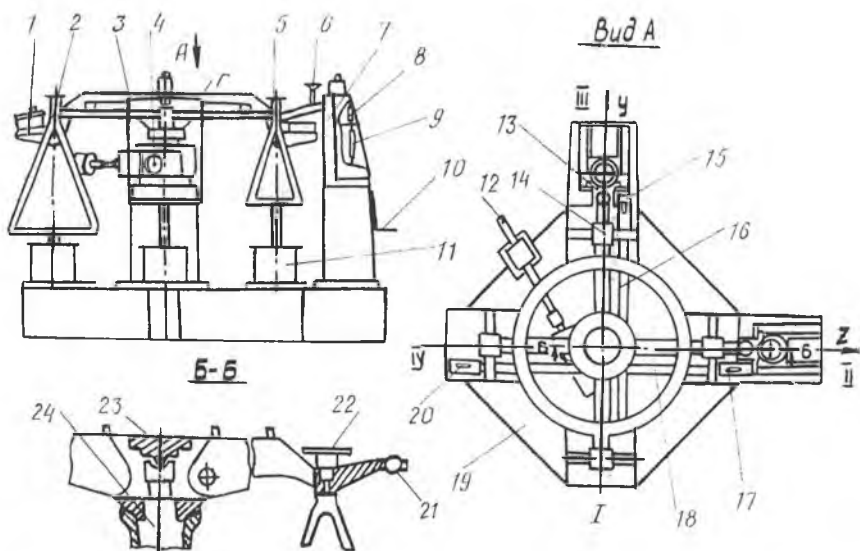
Конструктивная схема стола статической балансировки ССБ-7
